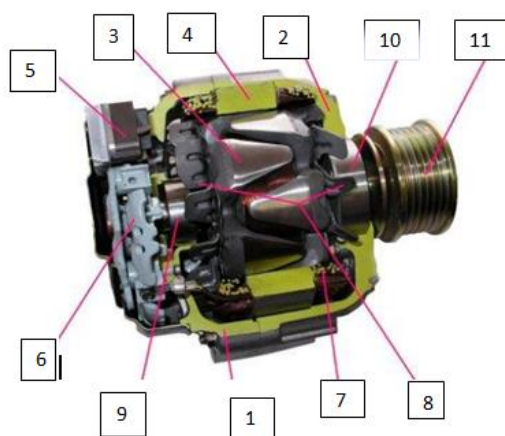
Конструкція сучасної генераторної установки: 1 – корпус задньої частини; 2 – корпус передньої частини; 3 – ротор; 4 – осердя статора; 5 – релерегулятор; 6 – діодний міст; 7 – статорна обмотка; 8 – крильчатка ротора; 9 – задній підшипник; 10 – передній підшипник; 11 – шків.
